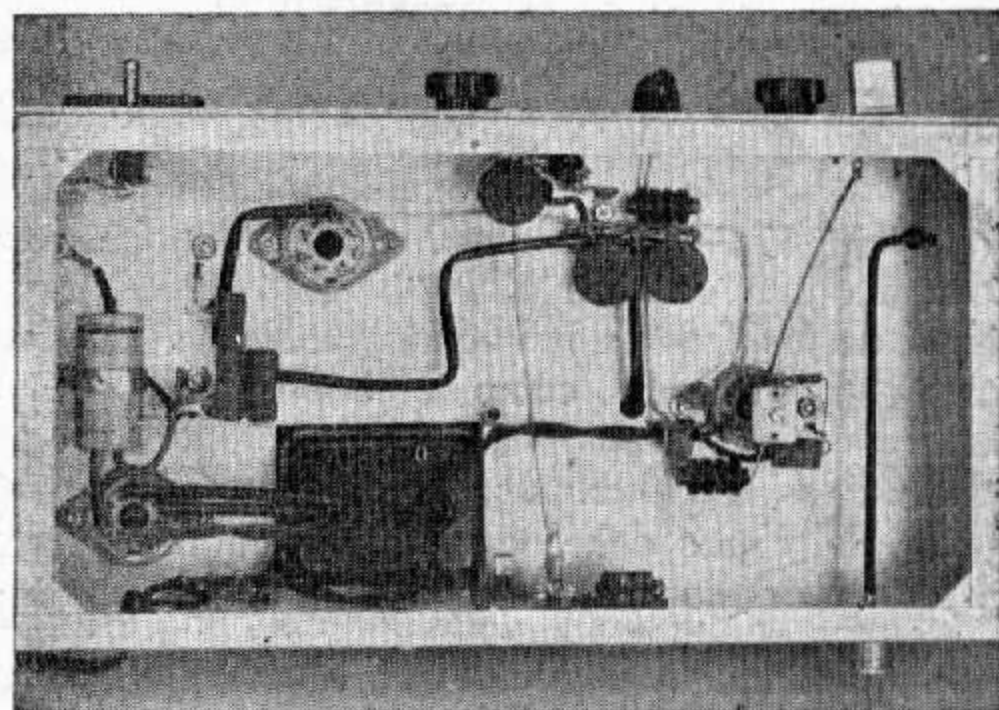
Vista de abajo del chasis. Los componentes de la fuente de alimentación ocupan la parte izquierda del chasis y el oscilador la parte derecha. El monitor de manipulación está montado sobre la aleta posterior del chasis. Aunque no se ve en la figura, los componentes del monitor están montados sobre una tira de cuatro terminales.
